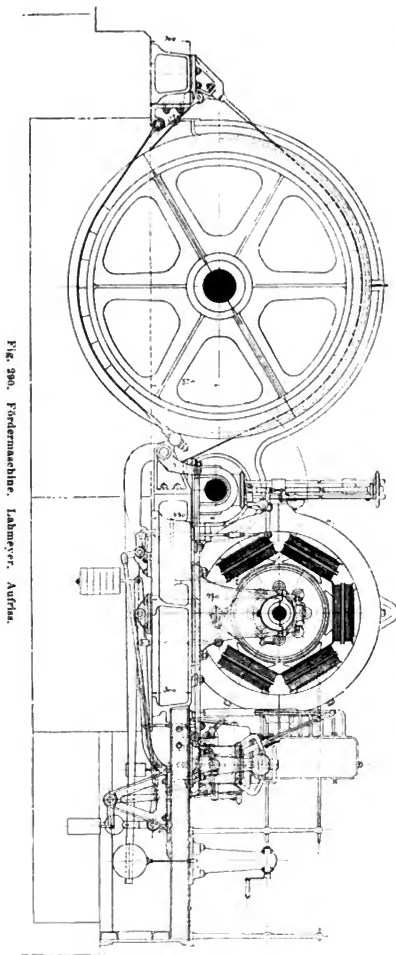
Fördermaschine. Lahmeyer. Aufsicht.
